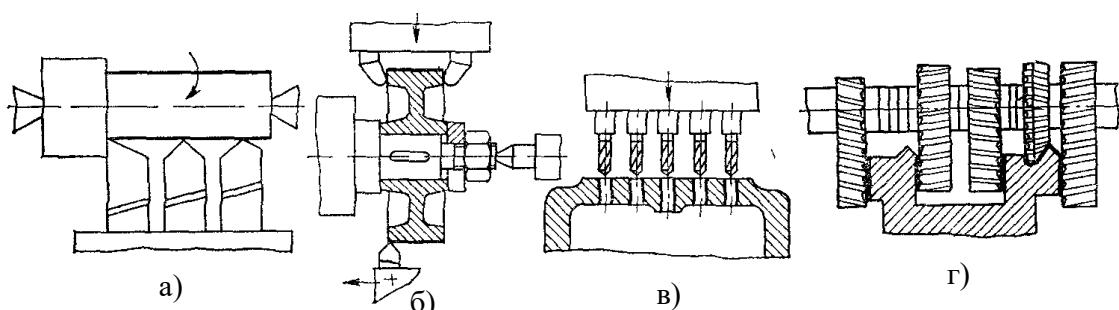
Схеми одномісної паралельної багатоінструментної обробки:
